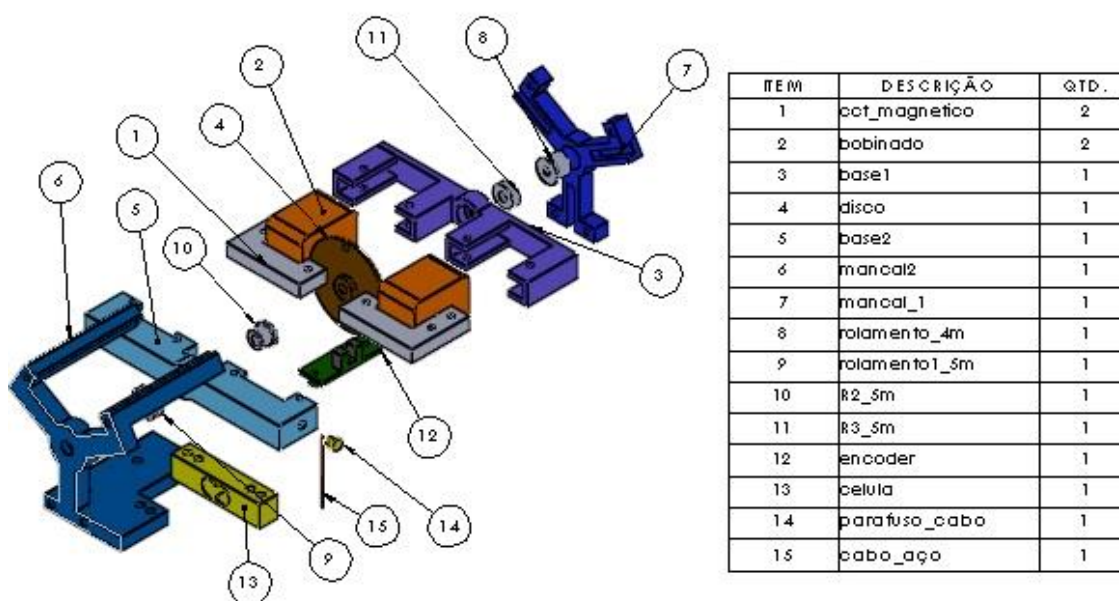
Vista explodida do sistema de frenagem, medição de torque e rotação.
